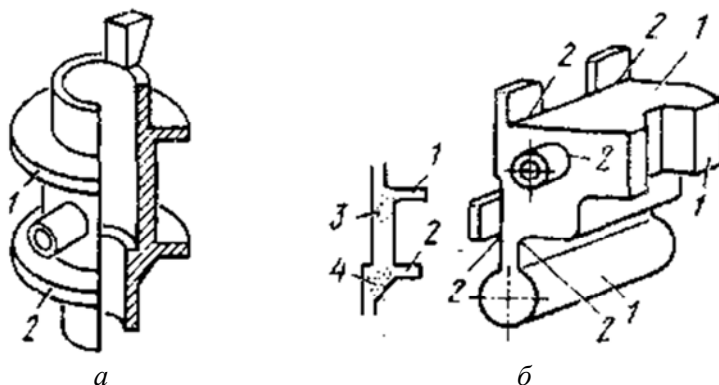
Нетехнологичные конструкции отливок втулки (а) и корпуса (б) из алюминиевого сплава
